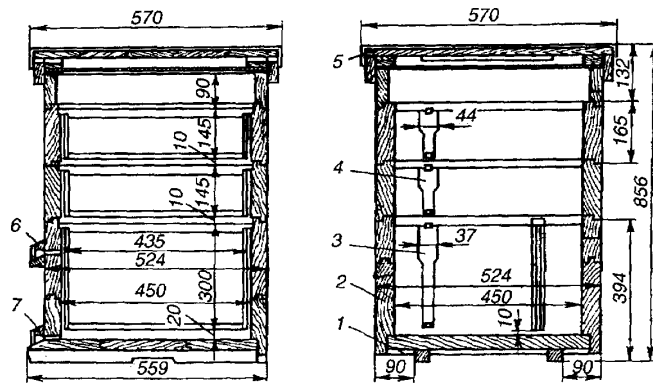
Улей однокорпусный с двумя магазинными надставками:
